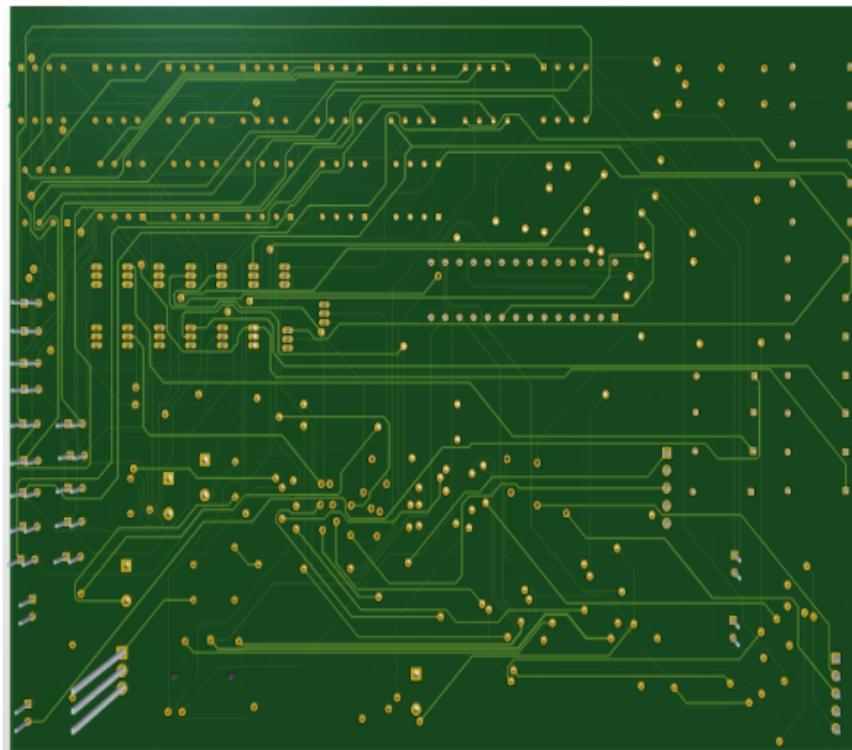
Vue 3D de la PCB : Bottom Layer
